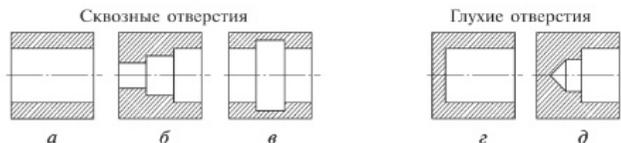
Формы цилиндрических отверстий: а, г — гладкие; б, д — ступенчатые; в — с канавкой
